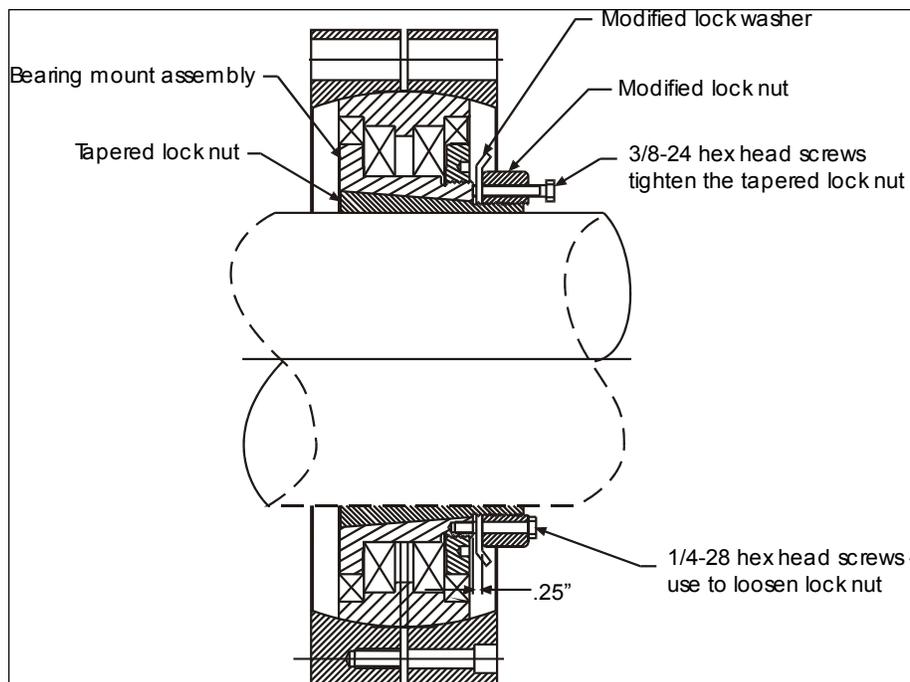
Die Lagerbaugruppen an die Bohrstange befestigen
